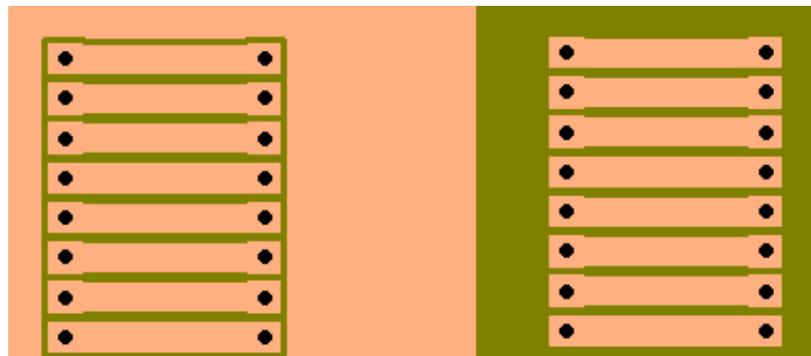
Parte final del engravamiento del circuito electrónico.
